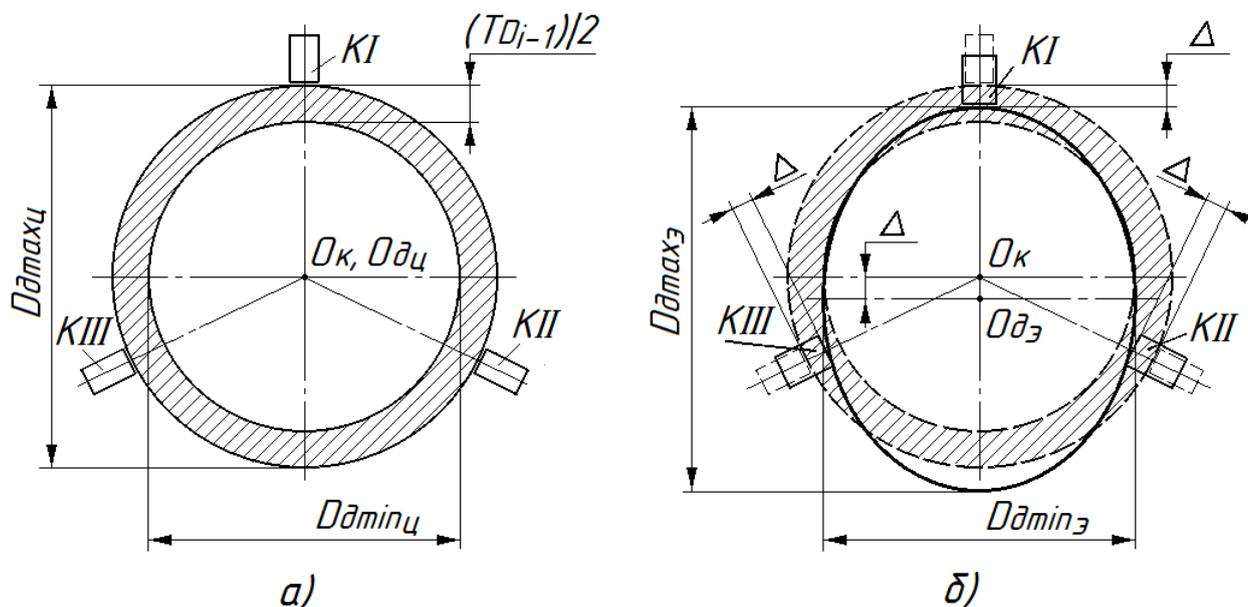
Исследовательская схема базирования детали цилиндрической формы по цилиндрической поверхности в трехкулачковом самоцентрирующем патроне: а) - схема базирования детали, имеющей геометрически правильную цилиндрическую форму; б) - схема базирования детали, имеющей форму эллиптического цилиндра
